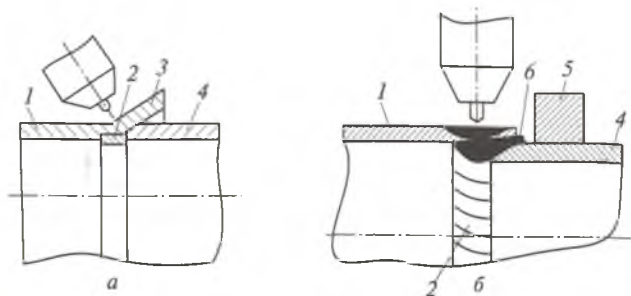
Схема подготовки к сварке титаноалюминиевого трубчатого переходника, собранного встык (а), и образования сварного шва на деталях, собранных внахлестку (б):
